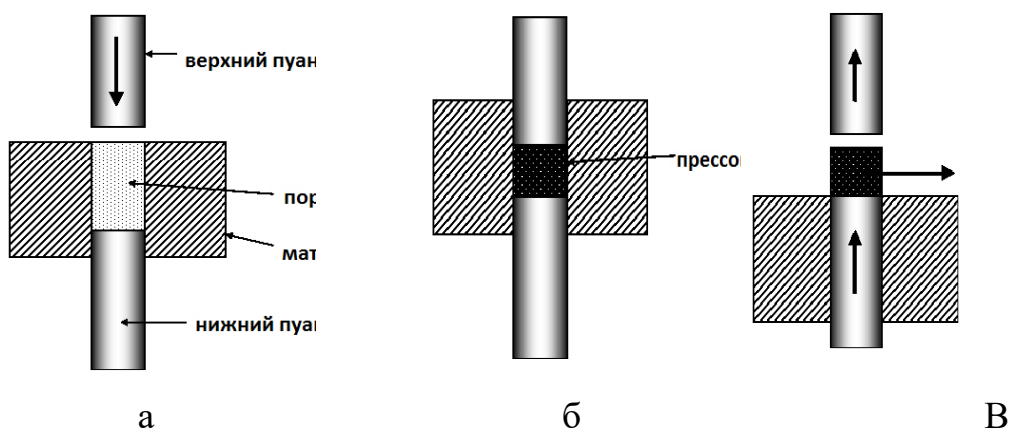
Стадии холодного прессования: а) засыпка порошка, б) прессование, в) выпрессовка
